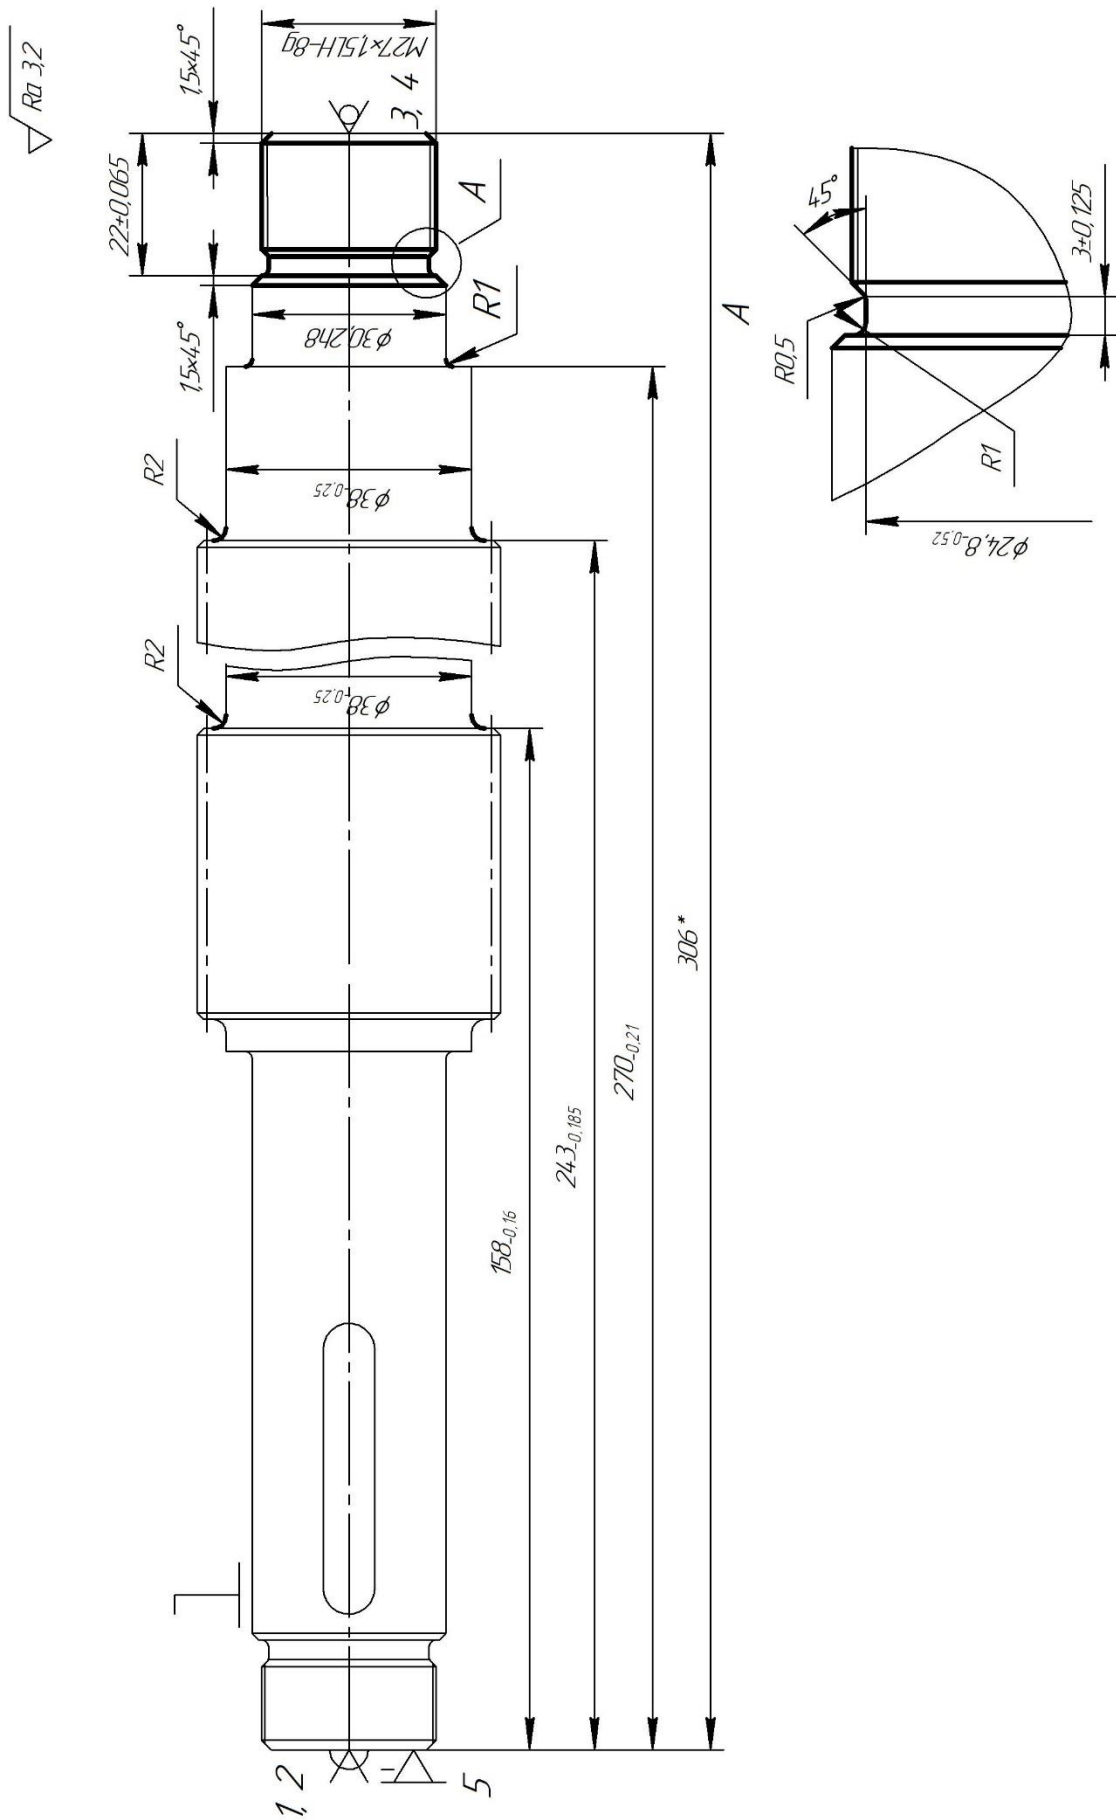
Схема базування заготовки на операції 065 токарній з ЧПК, установ Б
